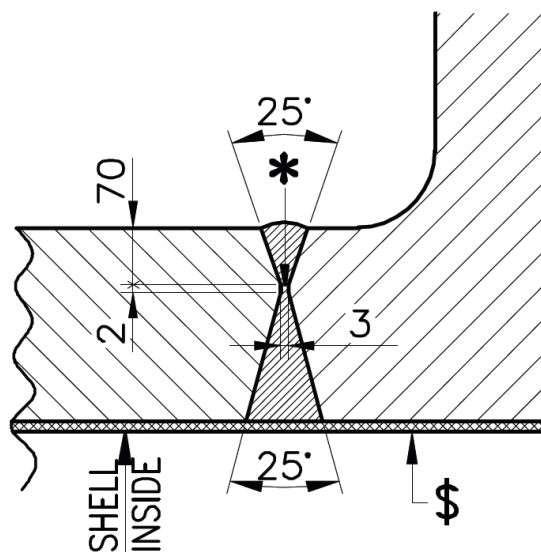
Detalhe das juntas soldadas entre casco e conexões do reator
